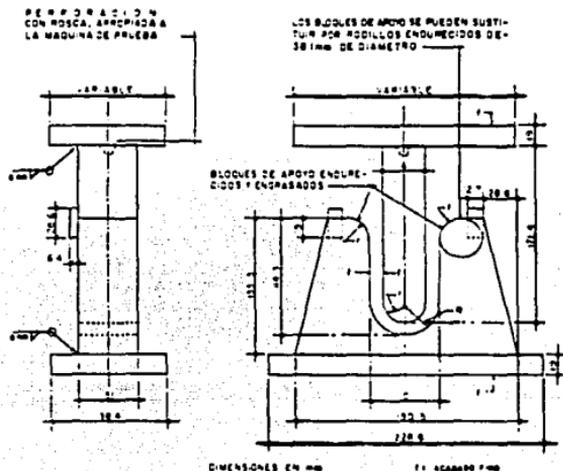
b) Prueba de doblado en soldadura de filete
